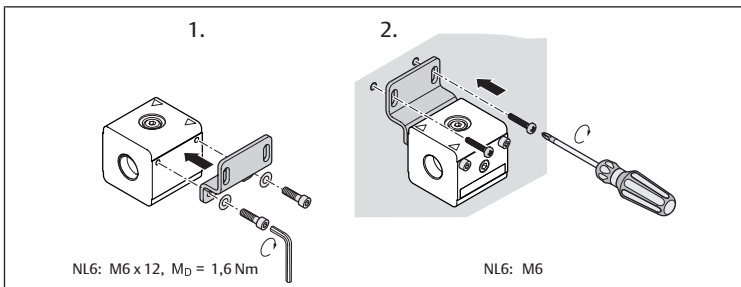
Befestigung mit Befestigungsplatte W01 | Serie NL6
